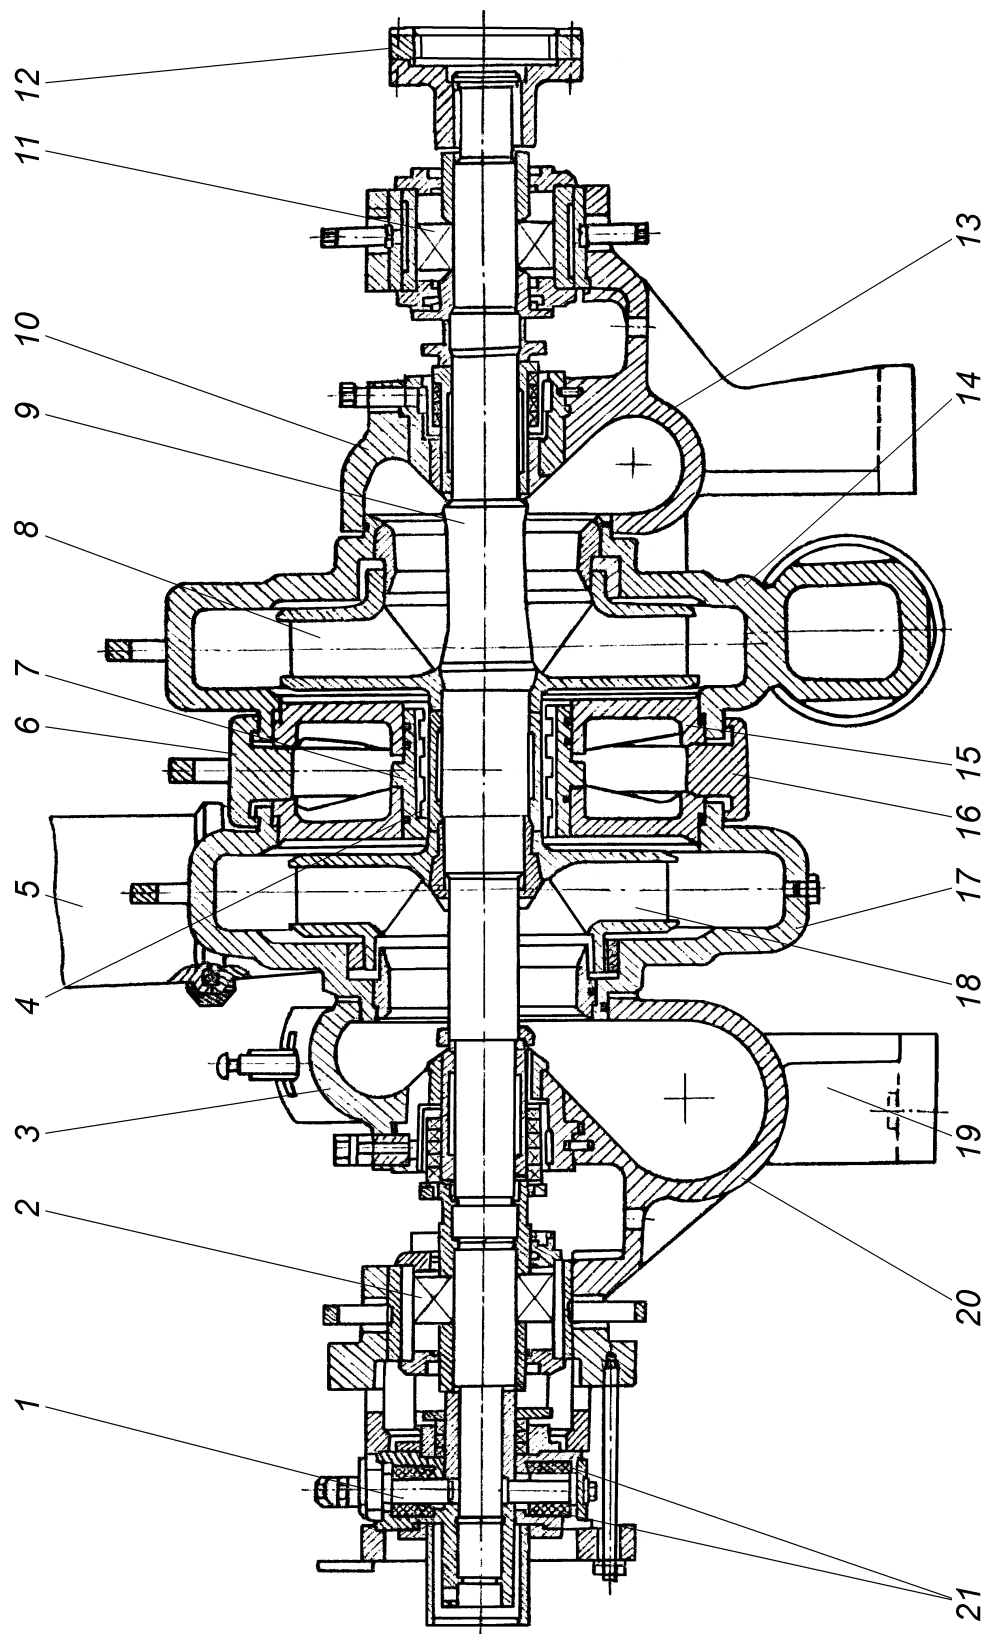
Вуглесос У900-325: 1 – п’ята; 2 – роликівий підшипник; 3 – кришка першої ступені; 4 – плаваючі втулки; 5 – перевідна труба; 6 – напівхомут; 7 – ущільнювальна втулка; 8 – робоче колесо другої ступені; 9 – вал; 10 – кришка другої ступені; 11 – роликівий підшипник; 12 – напівмуфта; 13 – підвід другої ступені; 14 – спіральний корпус другої ступені; 15 – бронедиски; 16 – напівхомут; 17 – спіральний корпус першої ступені; 18 – робоче колесо першої ступені; 19 – корпус; 20 – підвід першої ступені; 21 – підп’ятники
